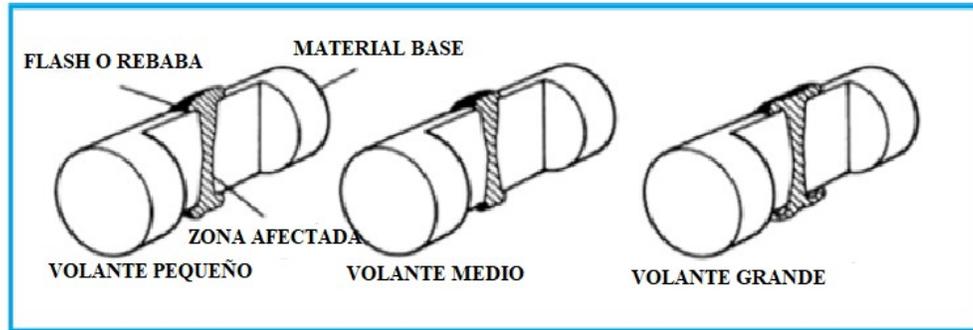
Influencia del tamaño del volante en el proceso de soldadura por fricción por inercia.
